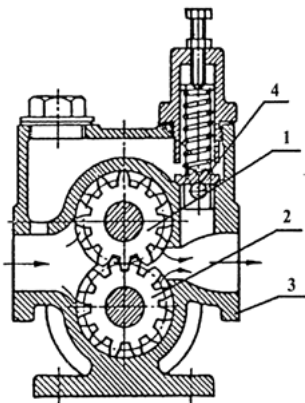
Схема зубчатого насоса: 1 — корпус; 2 — шестерня; 3 — корпус нагнетателя; 4 — предохранительный клапан
